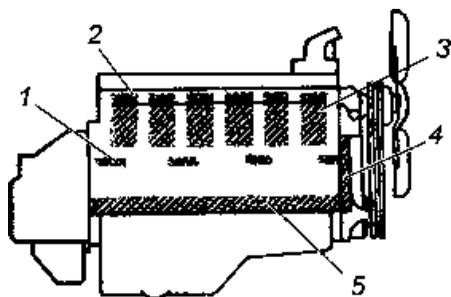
Зоны прослушивания двигателя для определения дефектов различных деталей: 1 — клапанов; 2 — поршневых пальцев, шатунных подшипников; 3 — распределительных зубчатых колес; 4 — коренных подшипников; 5 — подшипников распределительного вала
